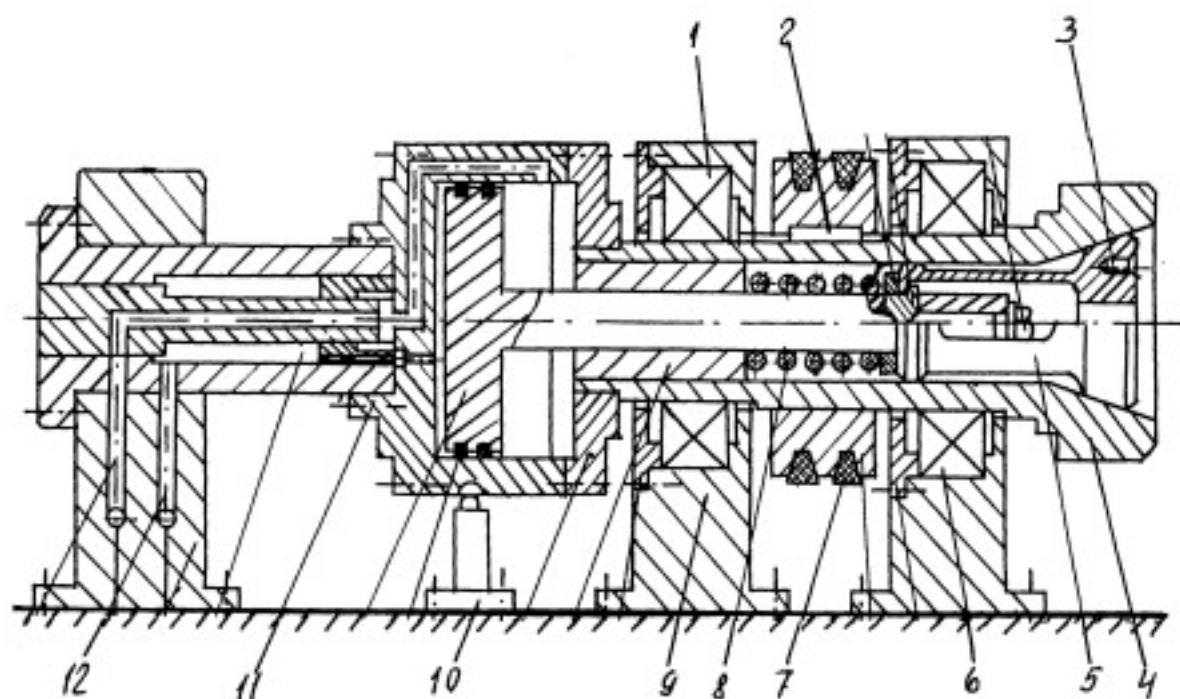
Загальний вид шпиндельного вузла для дослідження точності установки й базування ЗЦ у конус шпинделя
